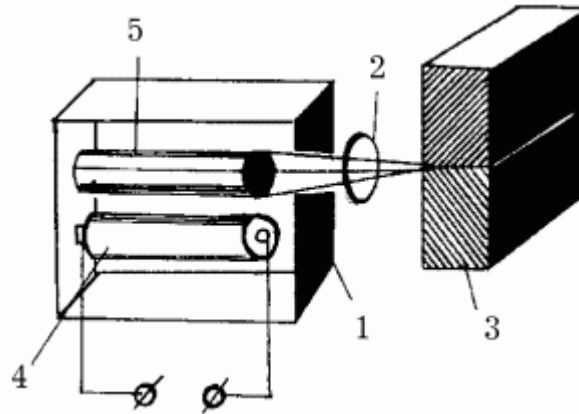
Лазерная сварка: 1 – излучение лазера; 2 – линза; 3 – свариваемые заготовки; 4 – лампа накачки; 5 – рубиновый стержень.
